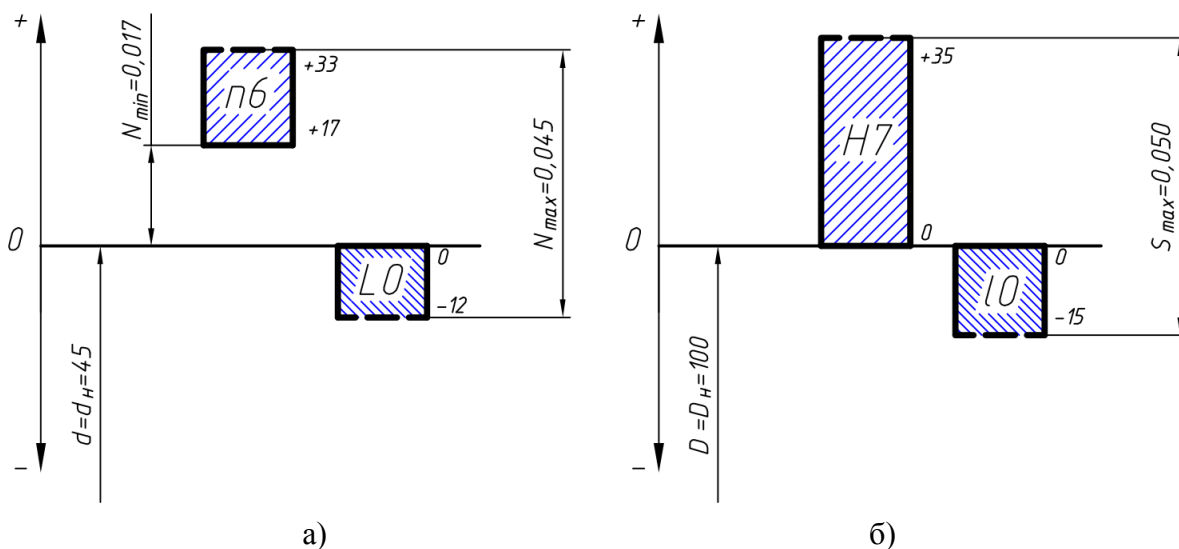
Схемы расположения интервалов допусков посадок для соединений:
